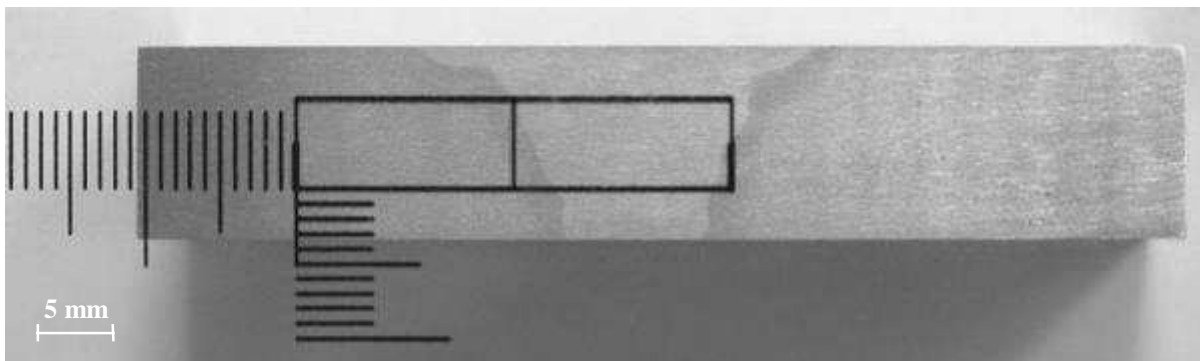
Exemple de bloc de prélèvement d'une éprouvette CT12Ep6. Un calque est superposé au joint soudé révélé par une attaque au Nital. Les positions de prélèvement de chaque éprouvette sont ainsi relevées, ici à 10,5 mm de la surface de gauche et à 3,25 mm de la surface inférieure sur la figure.
